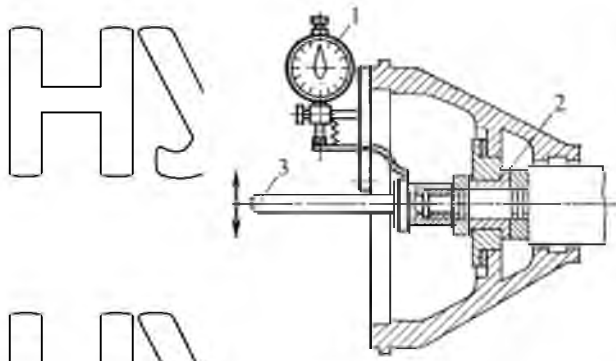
Схеми вимірювання зазору на масло в підшипниках турбокомпресора: 1-індикатор; 2-підшипник турбокомпресора; 3-рим
